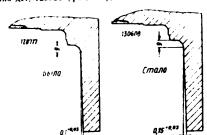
Замок гаск крепления упорного фланца и корпусов муфты вълючения и поршия храповика.
